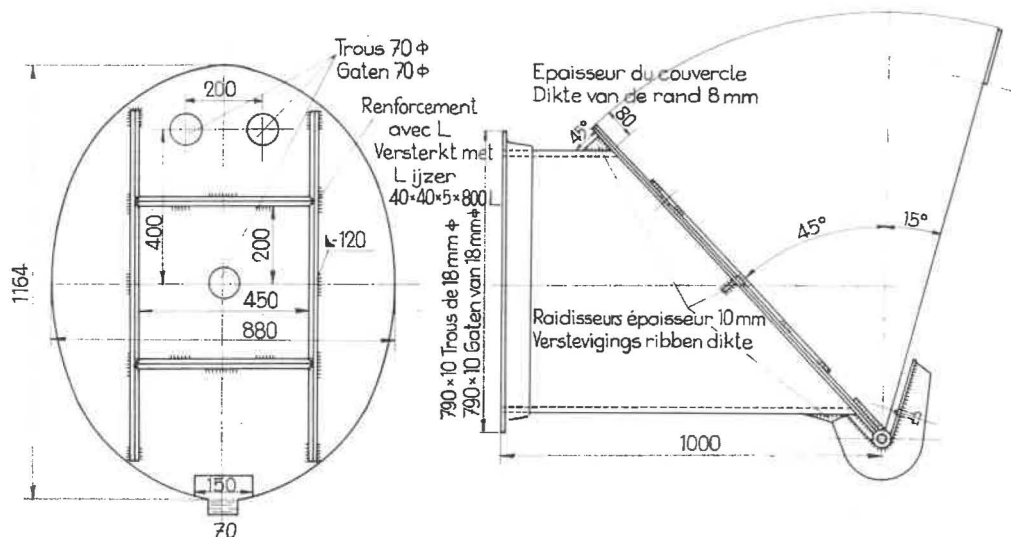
Konstruktieschema van de veiligheidssluitklep.
